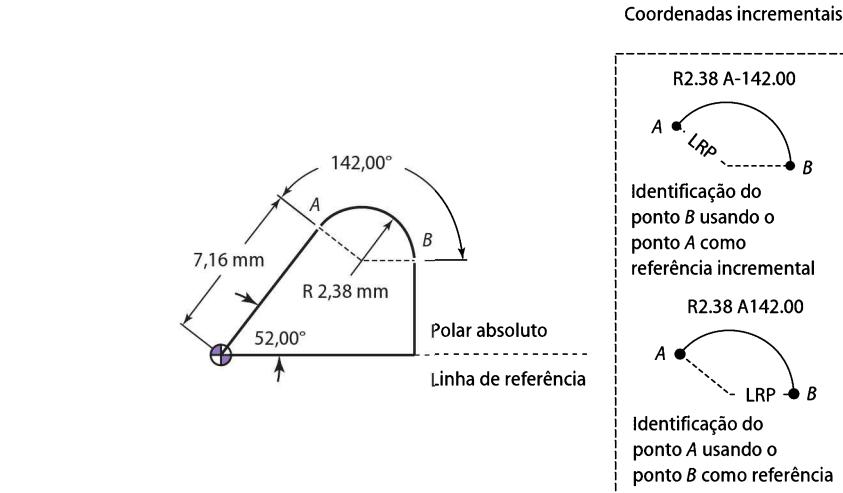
Algumas dimensões de desenho são polares, e não retangulares.
